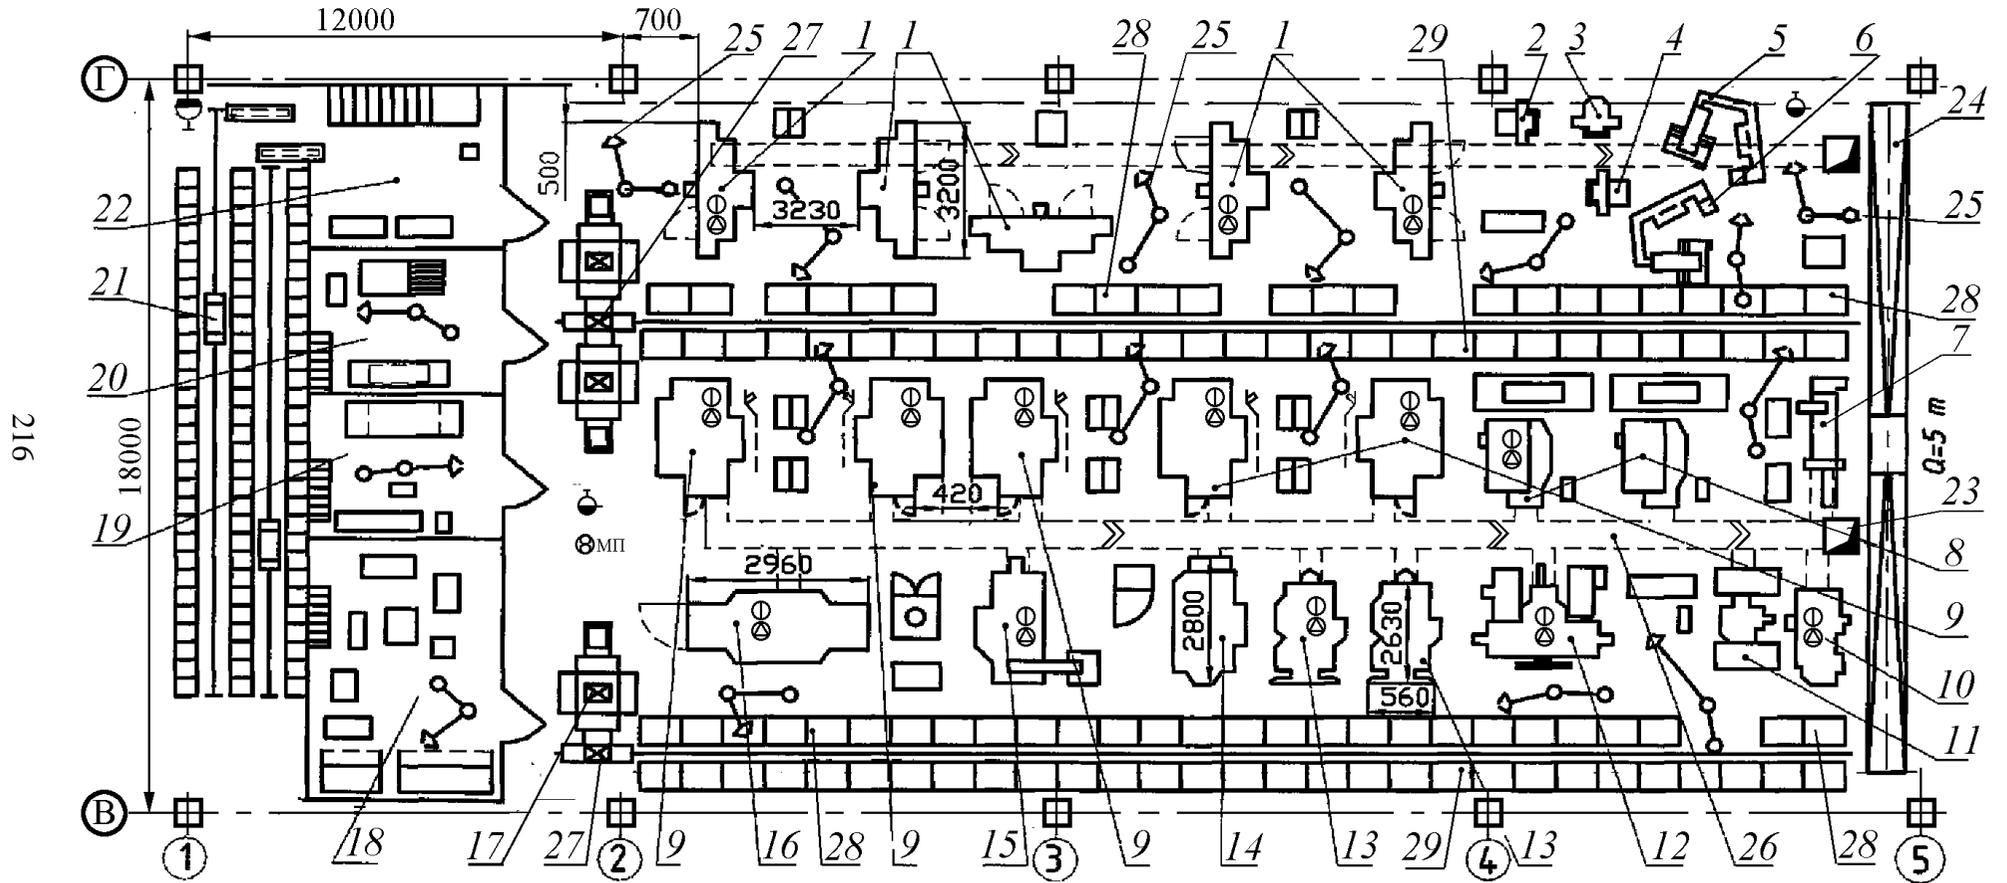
П14. ГПУ модели АТК-15 для изготовления валов, фланцев, шестерен, втулок, оправок, гильз:
